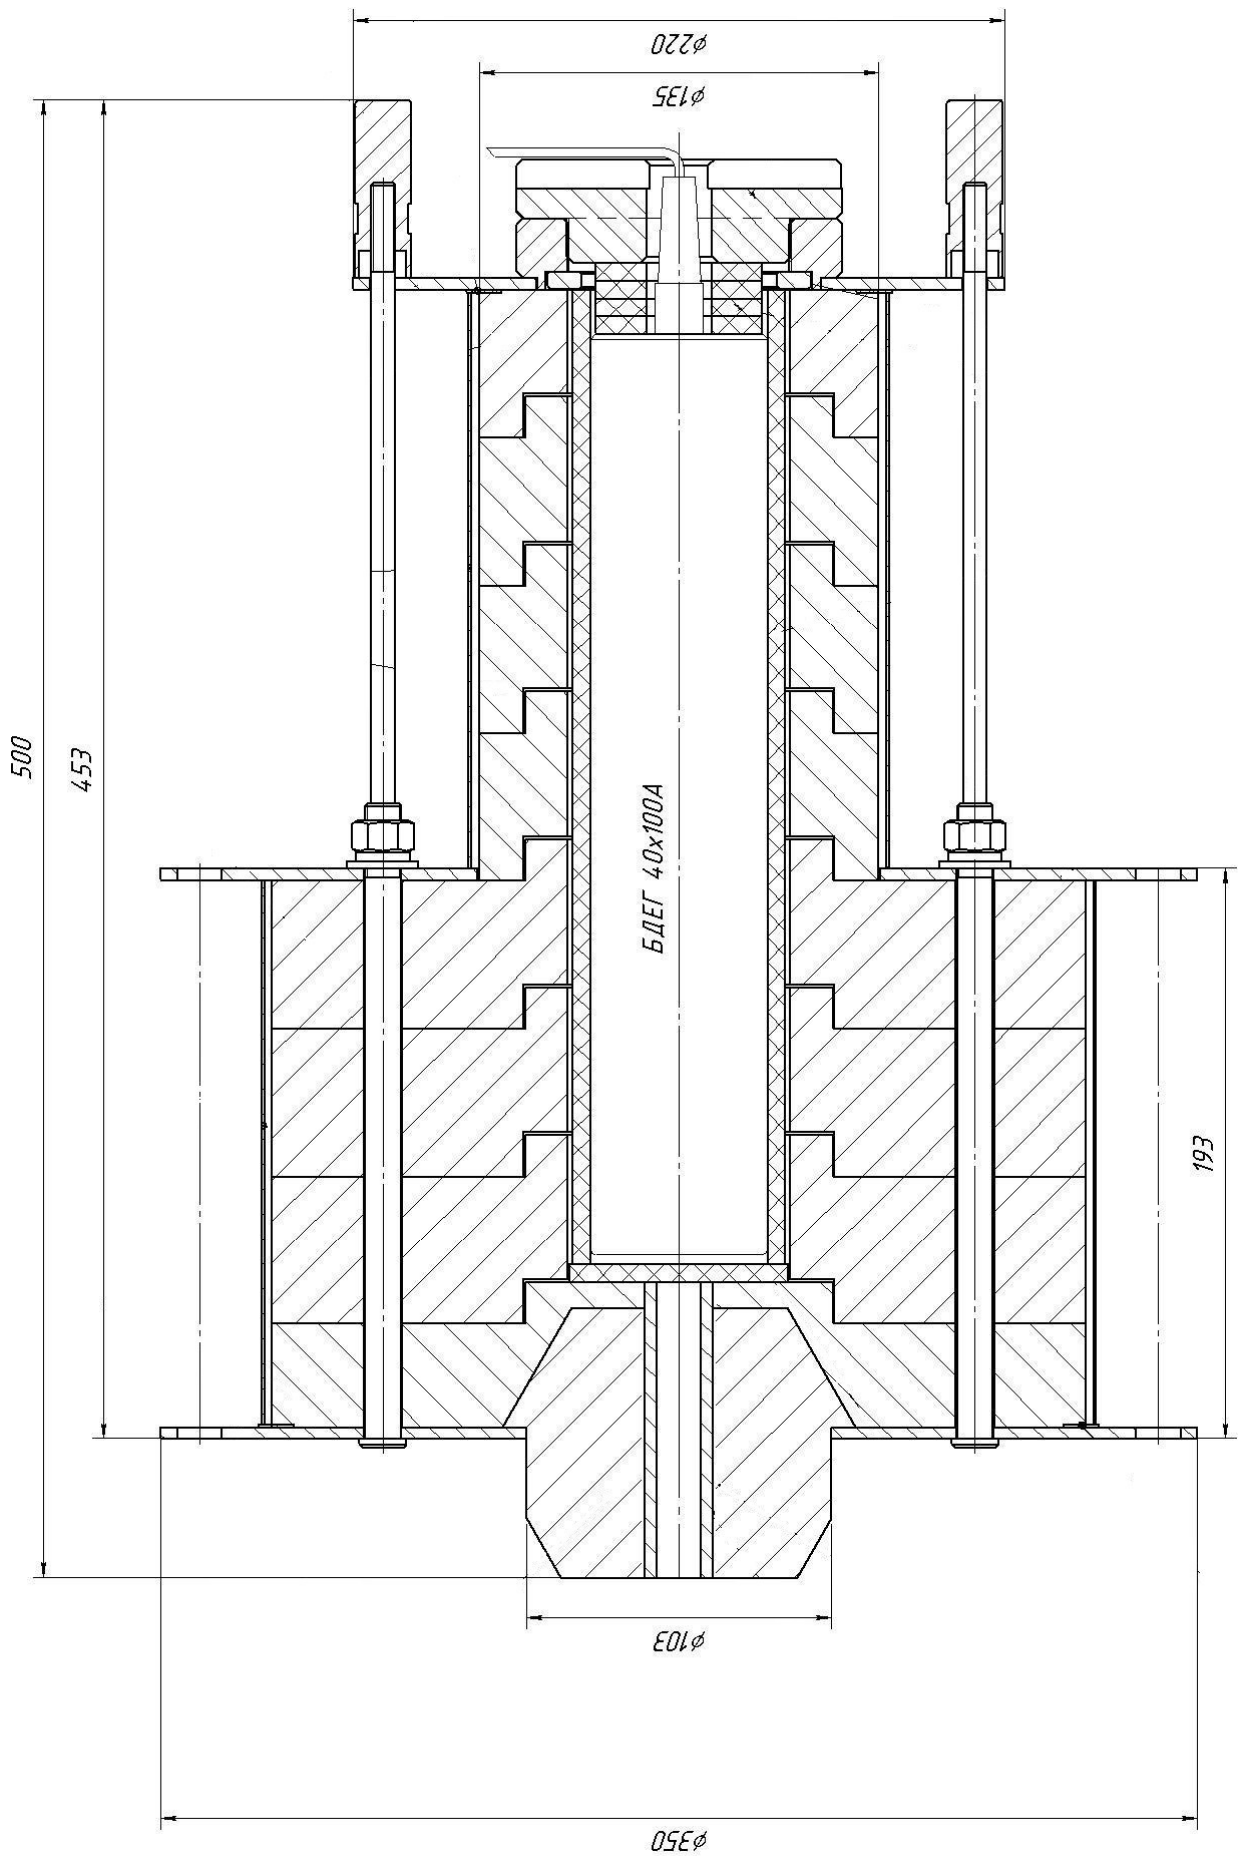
Коллимагор для труб ФВКМ.305179.005-01
